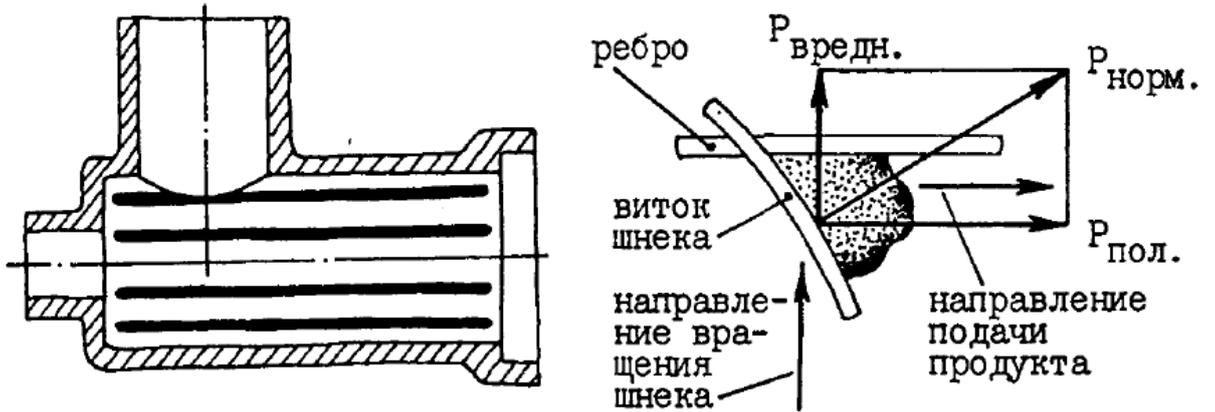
Корпус мясорубки с прямолинейными рёбрами
